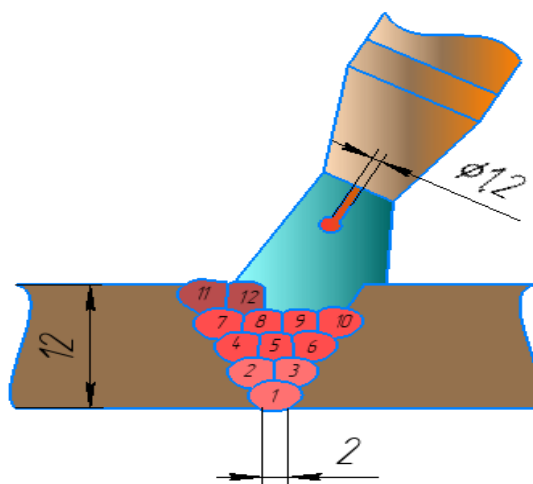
Схема наложения швов при сварке ДСПЭ
